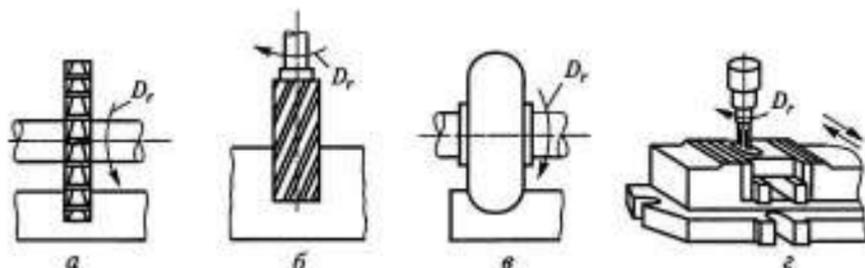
Схемы фрезерования прямоугольных и фасонных пазов: *а* — дисковые трехсторонние фрезы; *б* — дисковые пазовые или концевые фрезы; *в* — концевые фрезы; D_r — направление вращения фрезы
